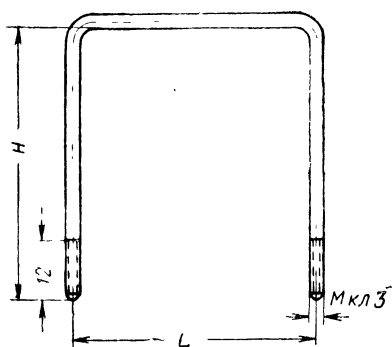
Конструкция и размеры, мм, скобы для крепления конденсаторов:
